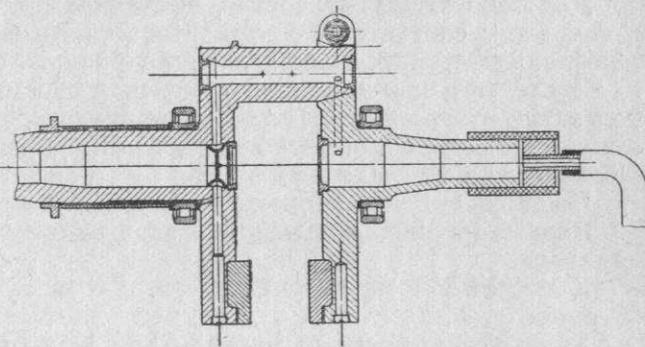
Коленчатый вал звездообразного мотора, подготовленный для испытания заглушек на герметичность.
